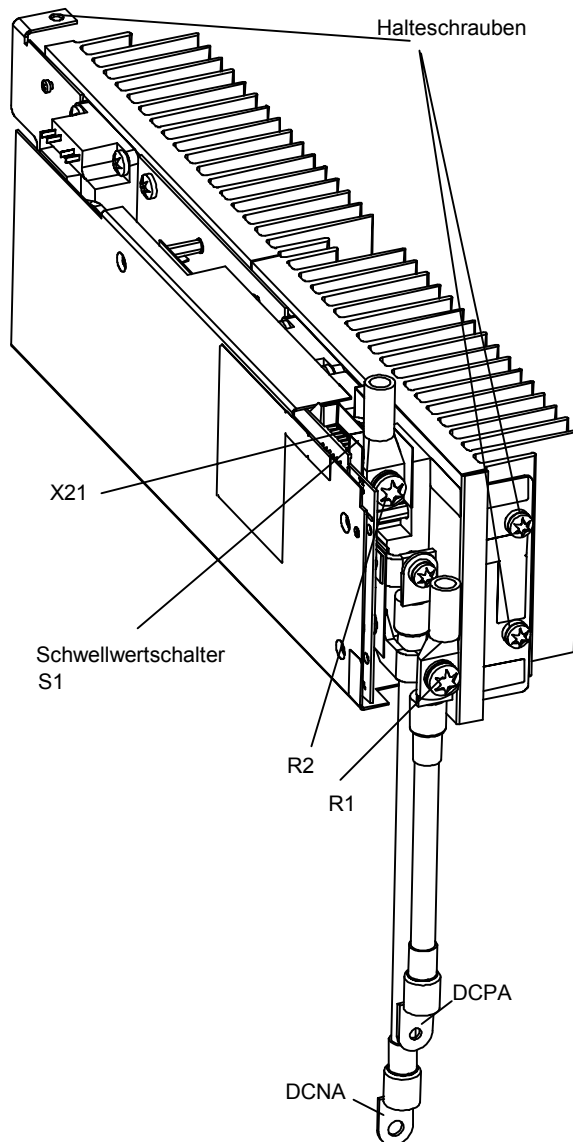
Braking Module für Active Line Module / Motor Module, Baugröße GX
